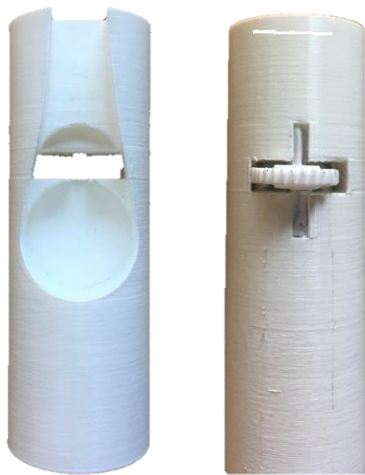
Corpo cilíndrico e roda dentada do segundo protótipo.
